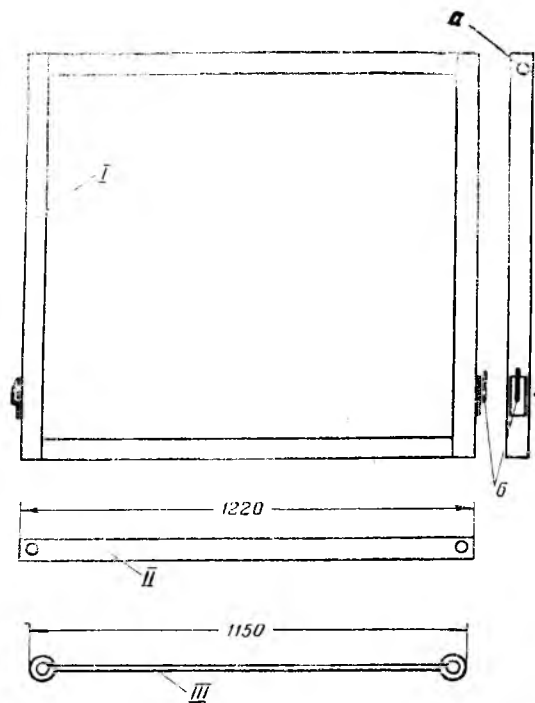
Части упаковочного ящика: I — рамы каркаса; II и III — скрепляющие детали.
